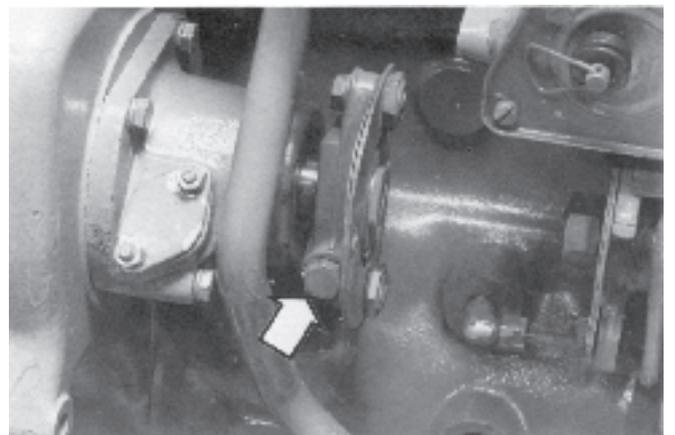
Vis de serrage pour le flasque d'entraînement avant
